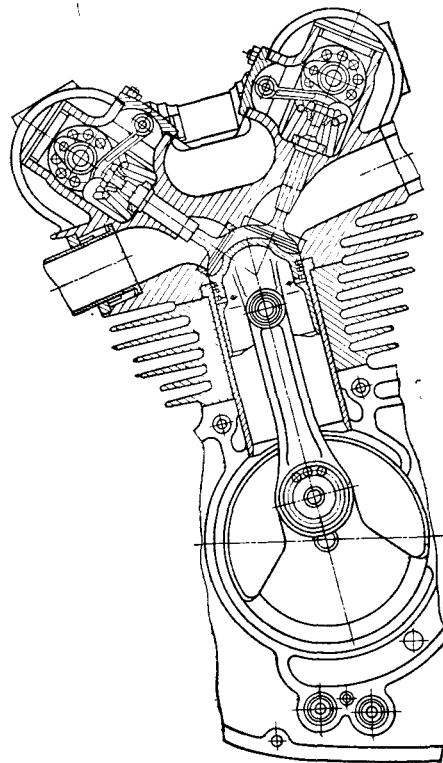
Механизм газораспределения двигателя С-159 с двумя верхними распределительными валами.
